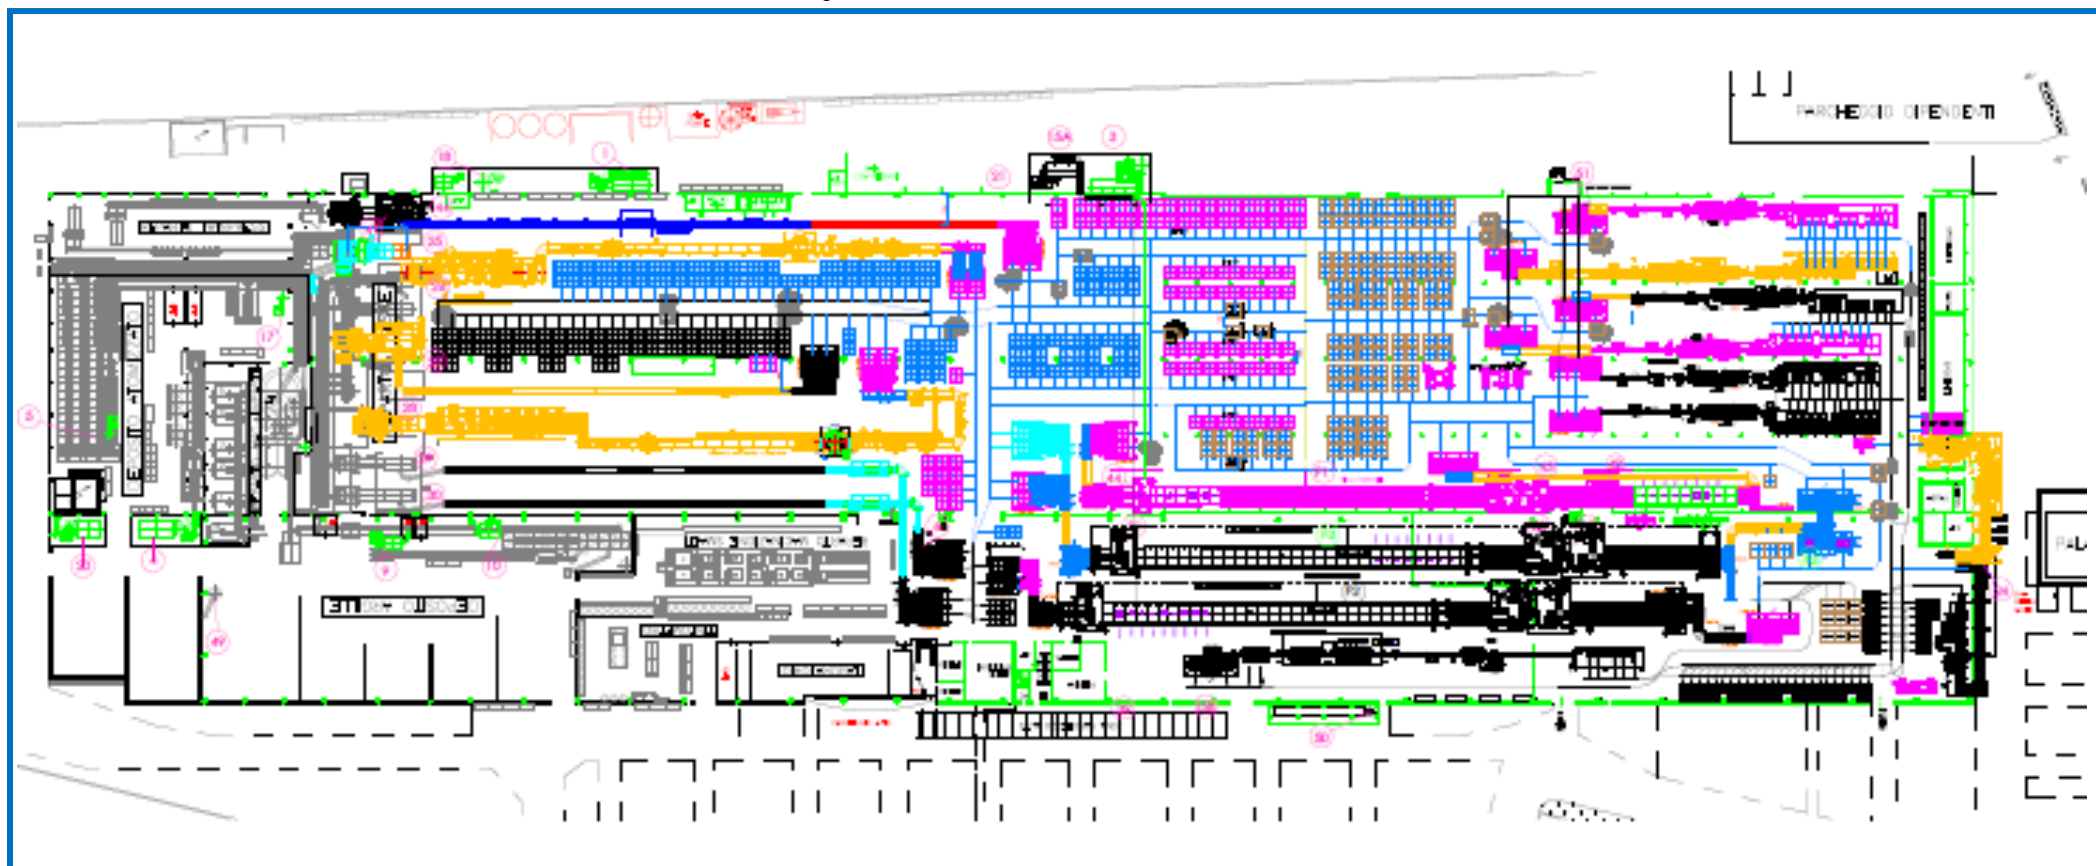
Vista aerea dell'area oggetto di collaudo
